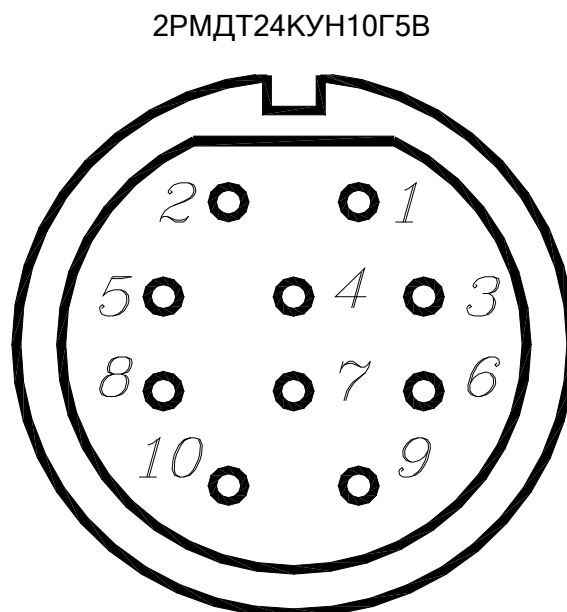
Нумерация контактов соединителя со стороны пайки
